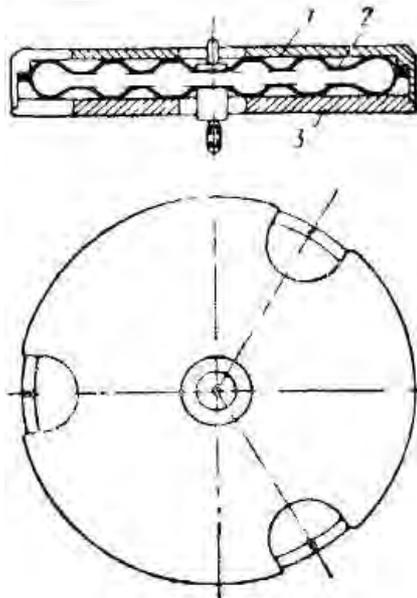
Приспособление для сварки мембран:
